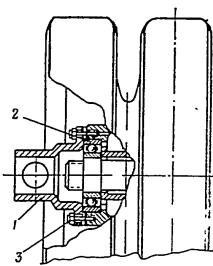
Установка катка: 1 — ключ; 2 — подшипник; 3 — болт
